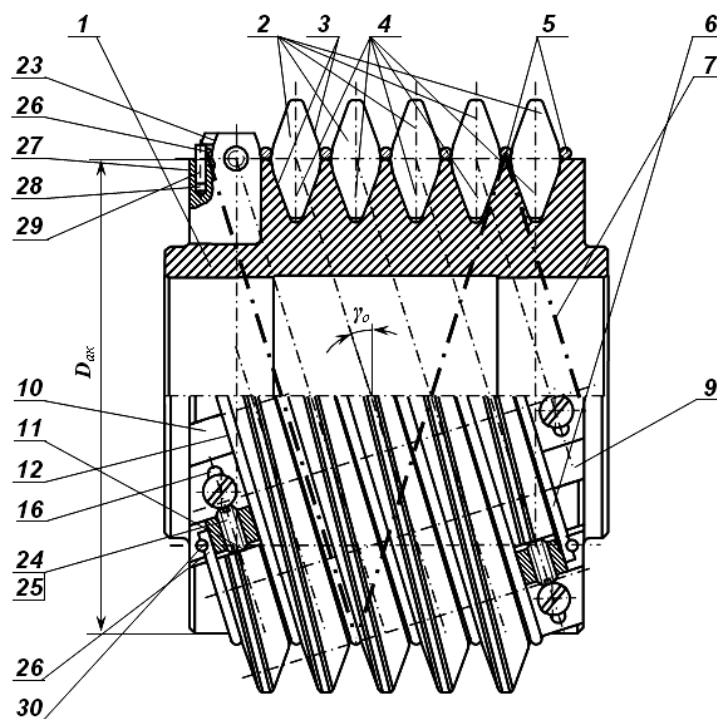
Сборная червячная фреза с пружинным креплением режущих пластин между витками ее корпуса
